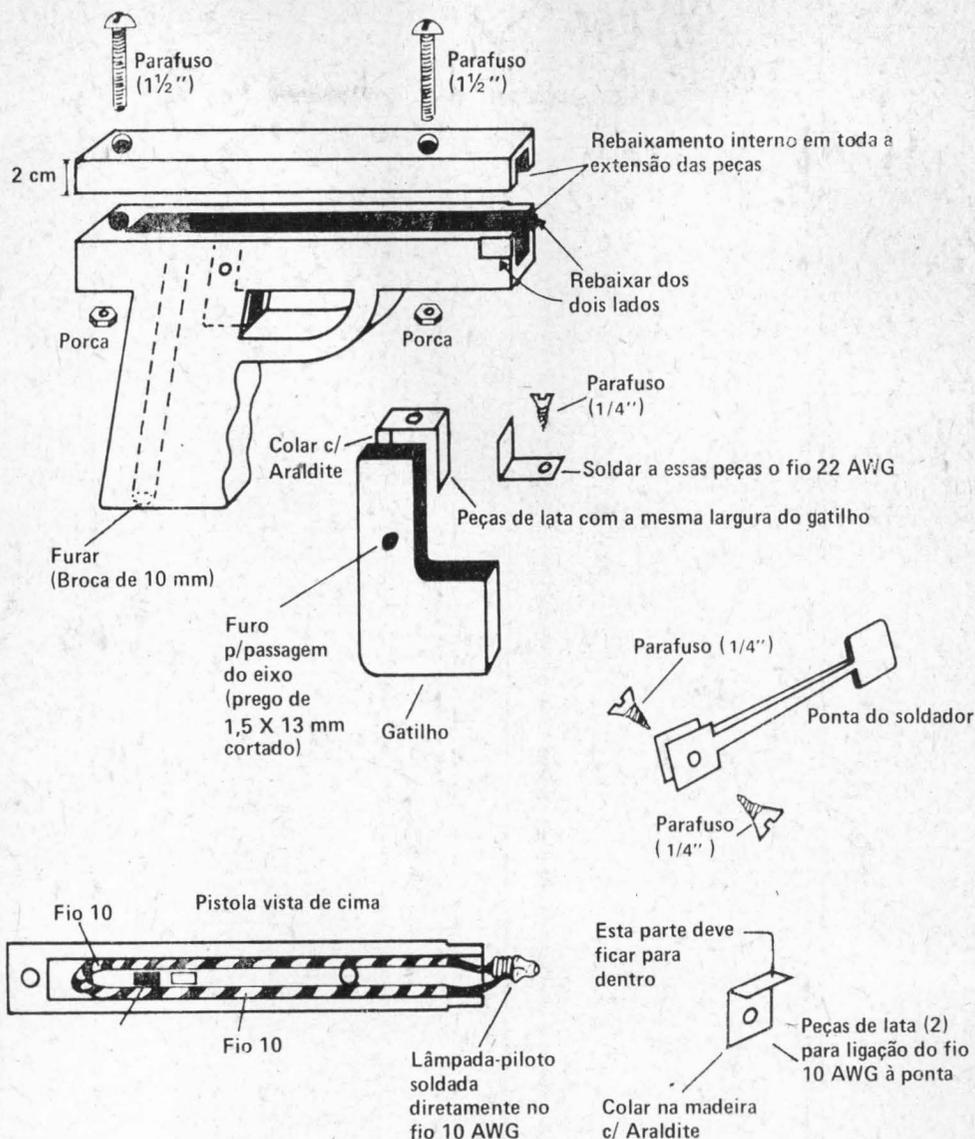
Vista das peças que compõem a pistola de soldar.
